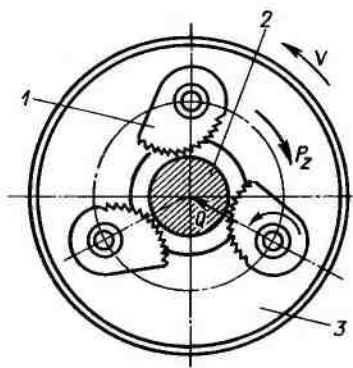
Схема работы трехкулачкового поводкового патрона:
